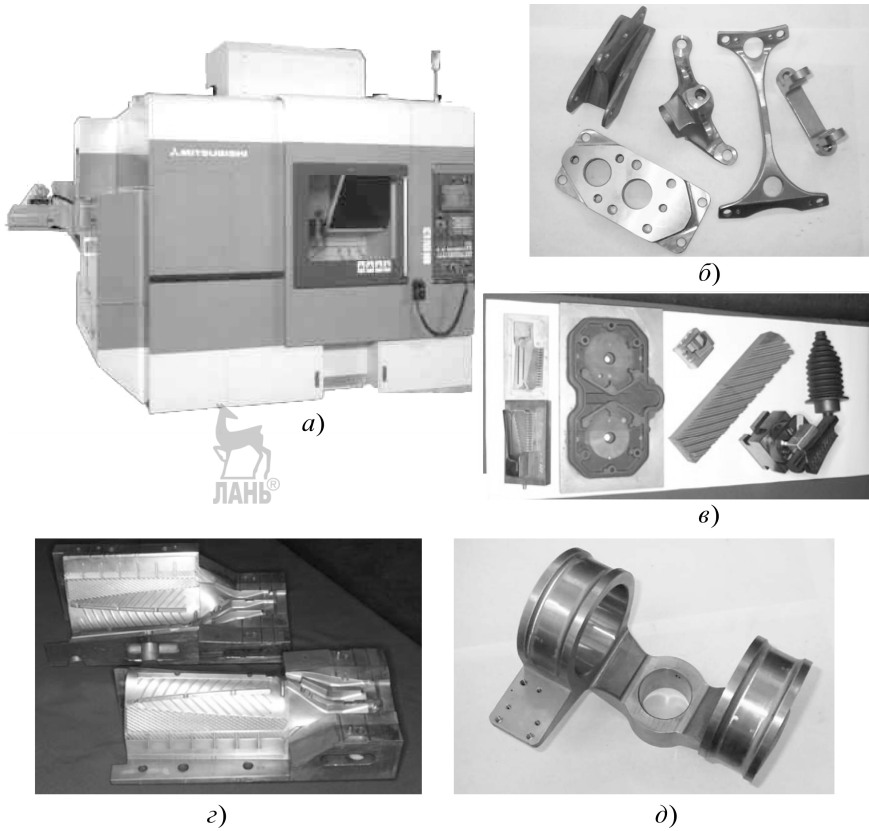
Обрабатывающий центр ZT1000/E130 и примеры обрабатываемых деталей
